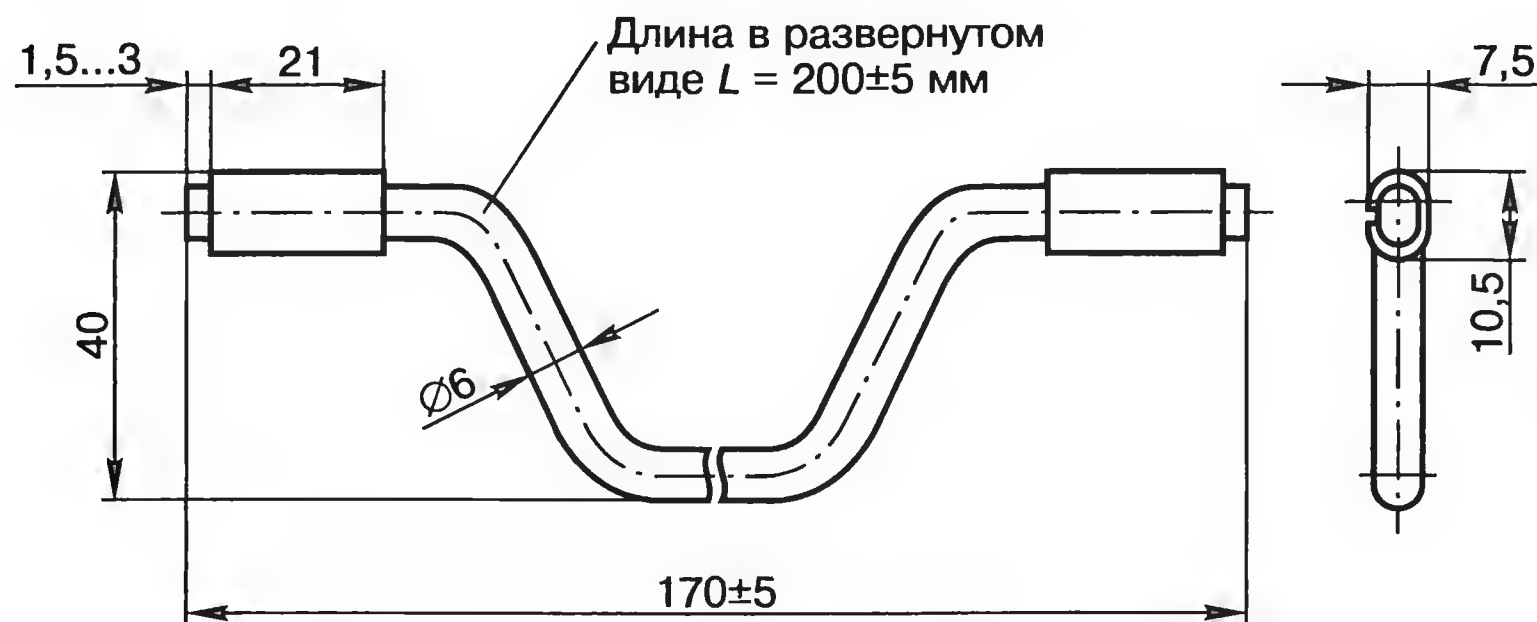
Соединитель рельсовый стыковой стальной приварной типа СРС-6
